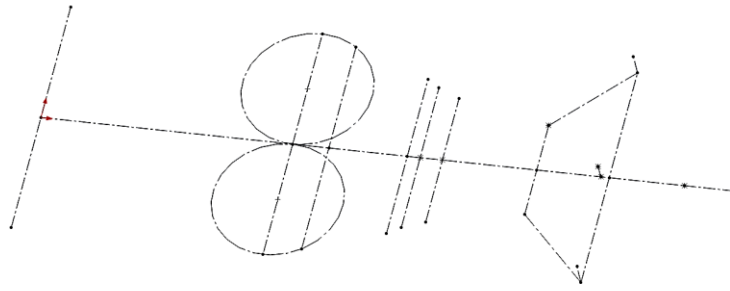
Croquis con geometrías constructivas de referencia.
